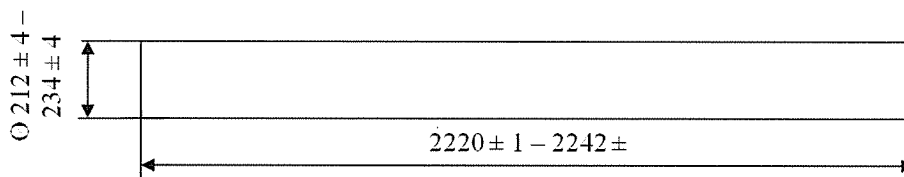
Загальний вигляд круглої заготовки попередньо механічно обробленої для виготовлення осі чорнової
